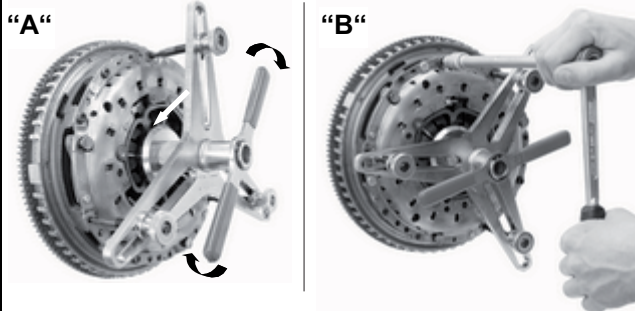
Druckspindel zurückdrehen, Spannvorrichtung abnehmen.
